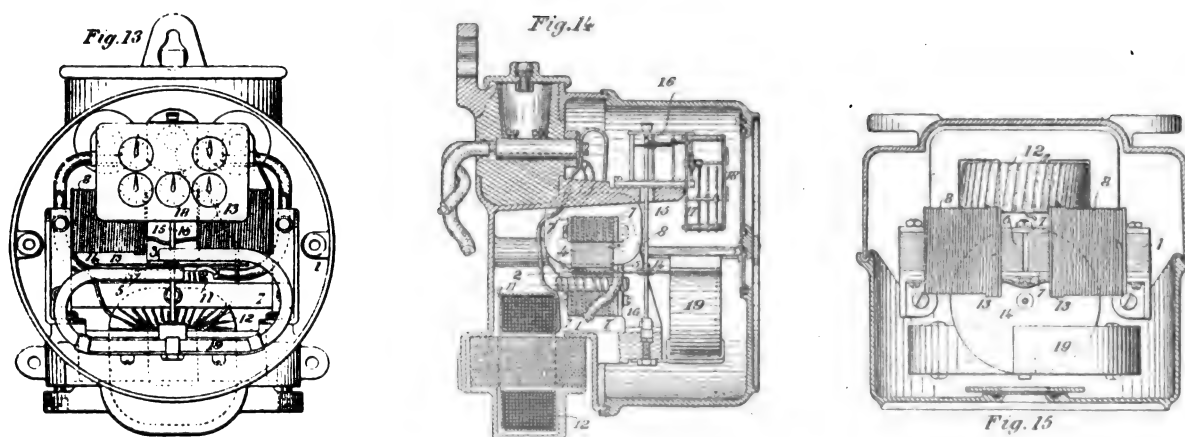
, 14 et 15. — Élévation, coupe verticale et plan du compteur Davis et Conrad.
